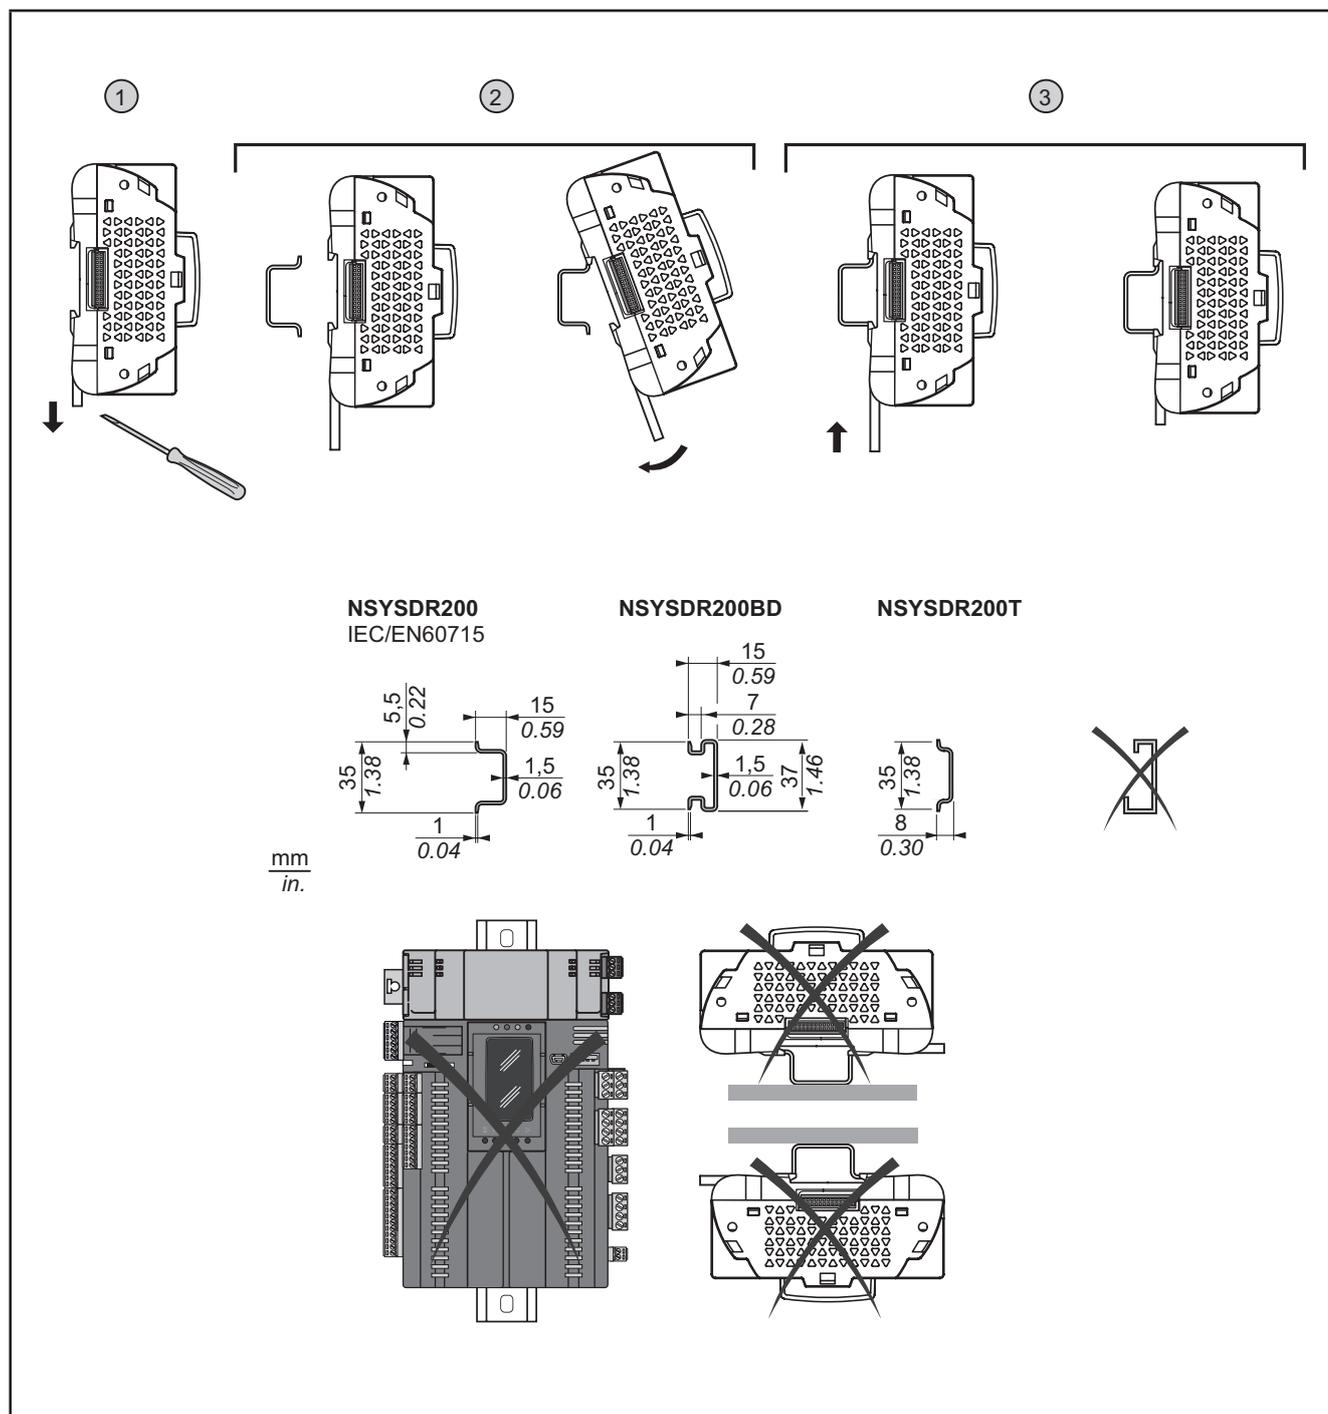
Montaggio di EWCM 9000 PRO (HF) su guida DIN
